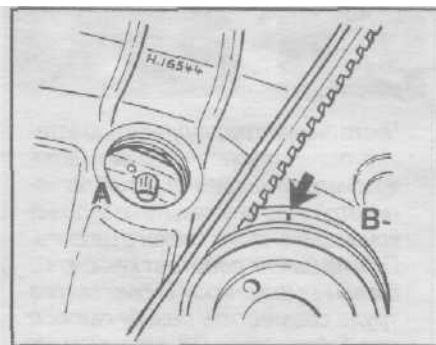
, б. Метки верхней мертвой точки - двигателя 1,6 и 1,8 литра
